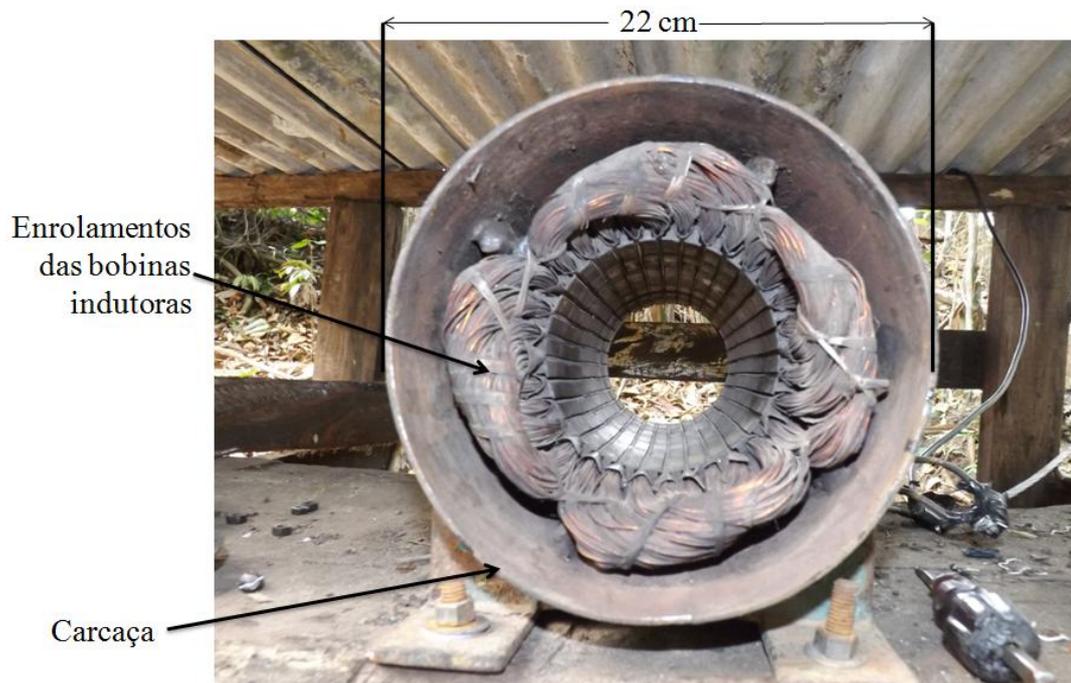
Vista interna do dispositivo gerador. O estator, ou seja, a parte imóvel é mostrada em destaque
